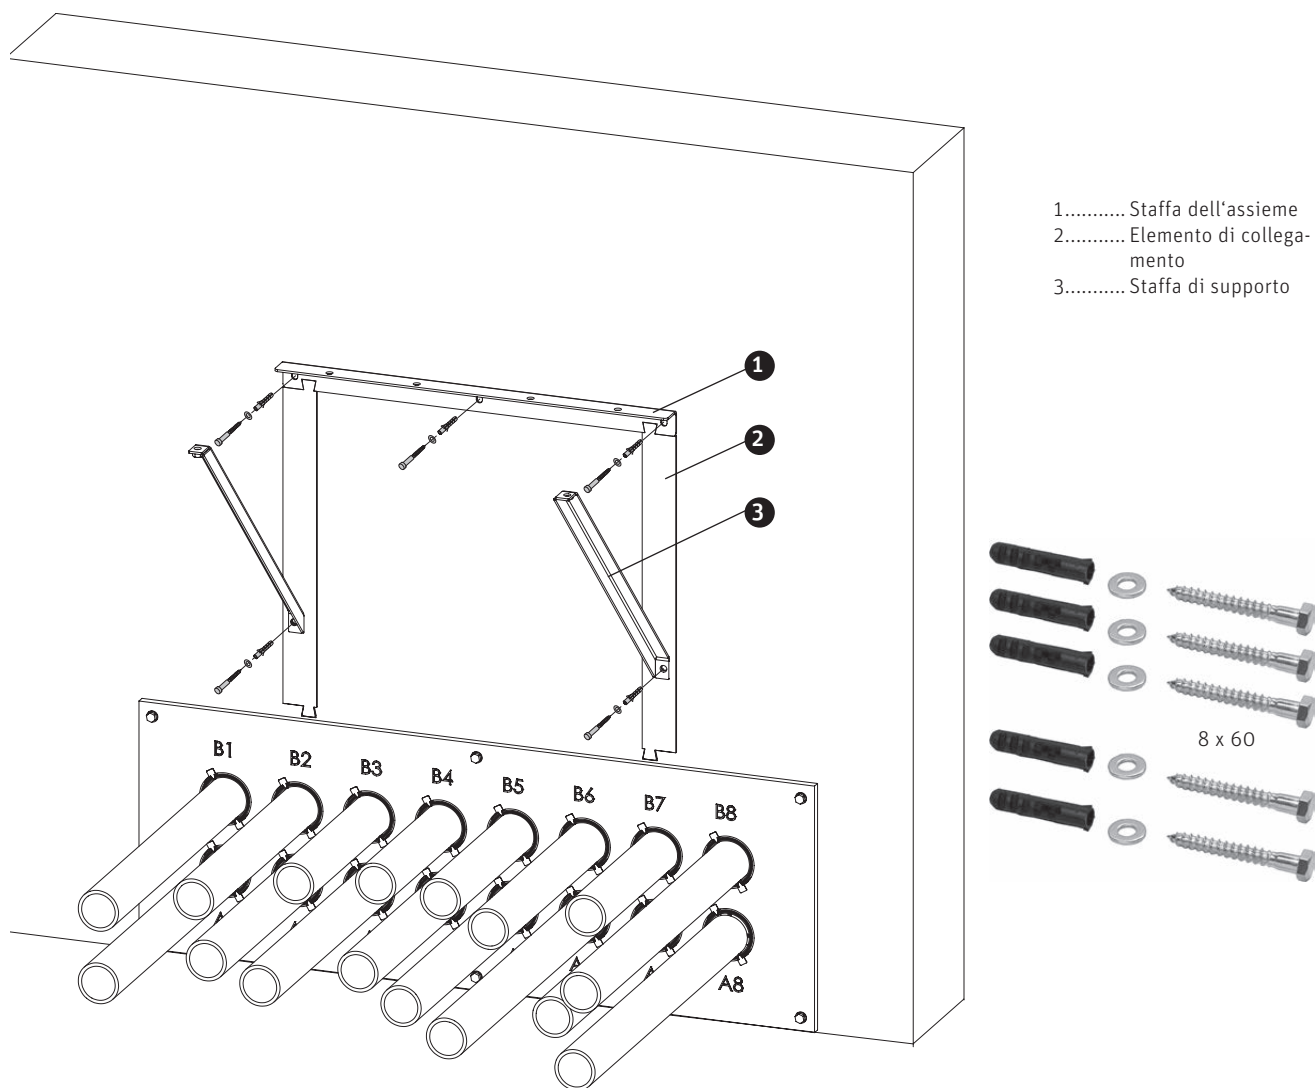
Montaggio di angolare di montaggio, elemento di collegamento e angolare di supporto
